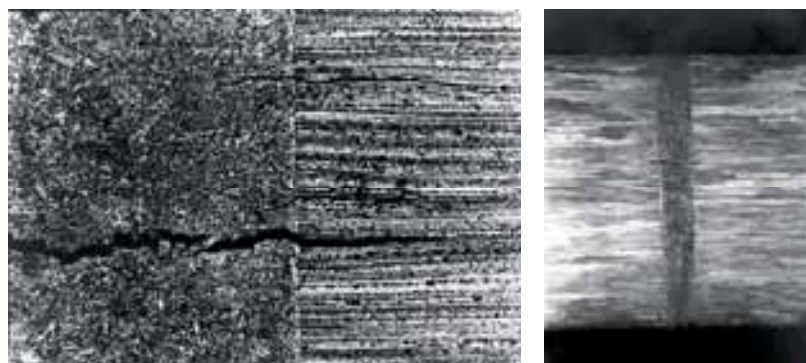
, 46: Bei großer Schweißtiefe und hoher Schweiß-Geschwindigkeit können sowohl Heiß- wie Schrumpfrisse auftreten (Al Mg Si 1).
